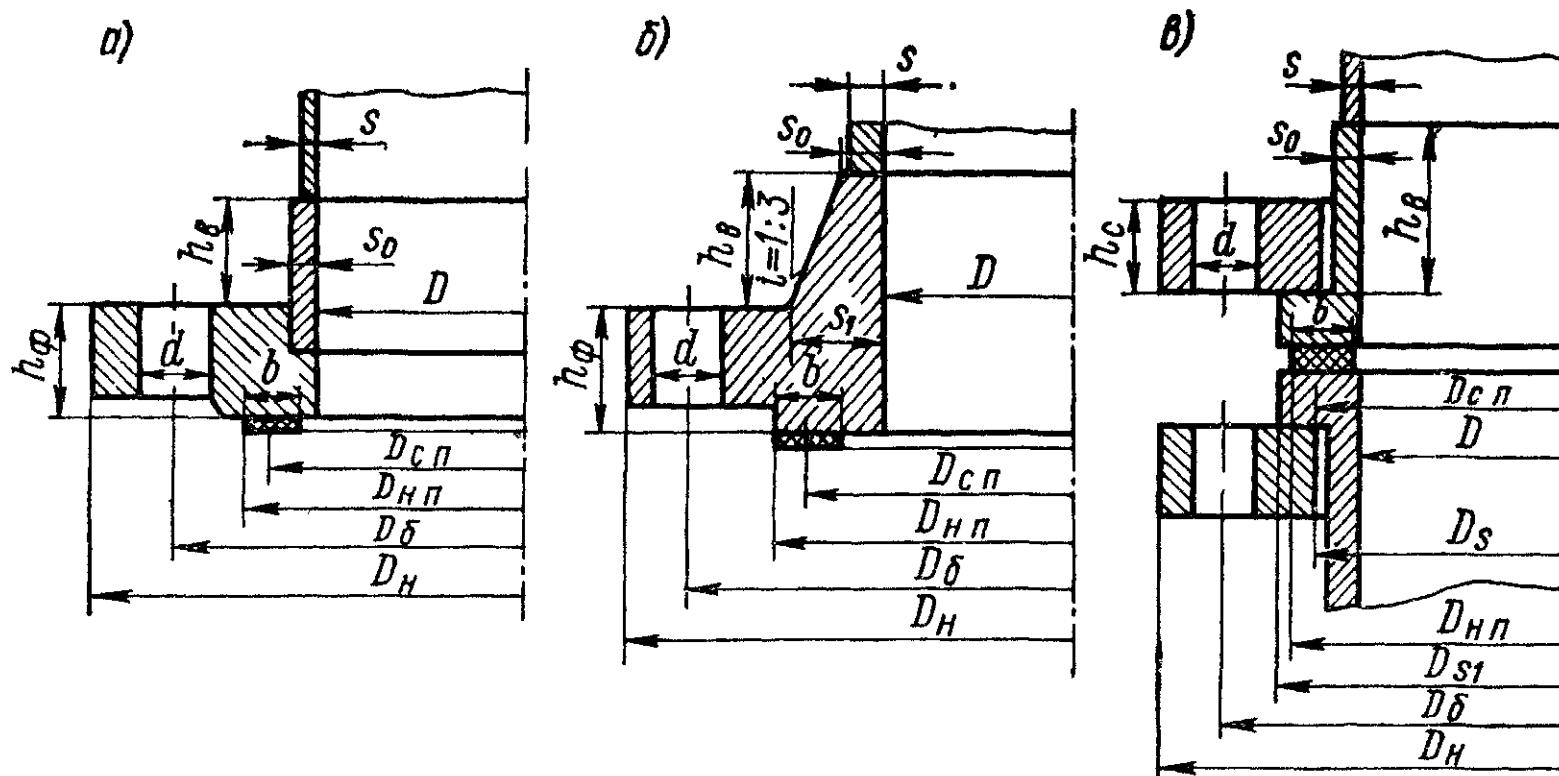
Типы фланцев: а — плоский приварной; б — приварной встык; в — свободный
